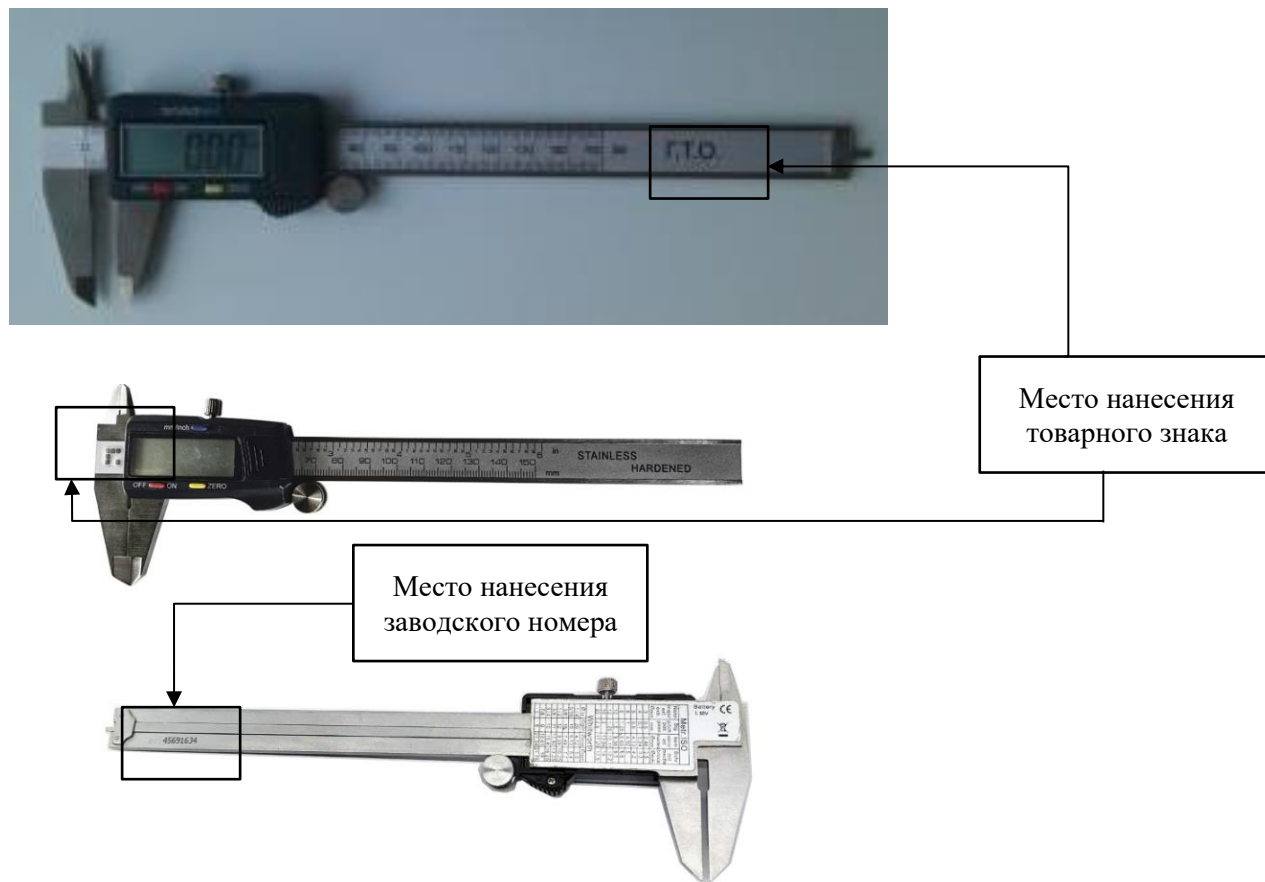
Общий вид штангенциркулей цифровых с глубиномером
